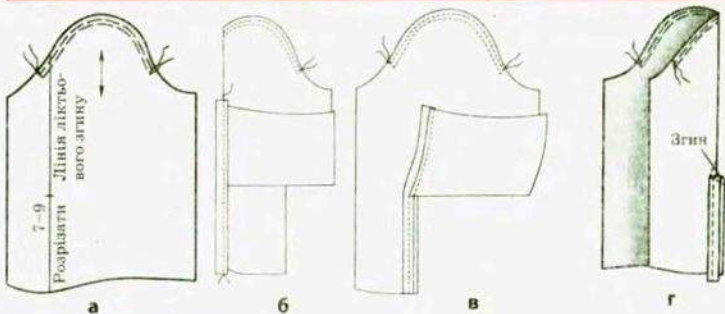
Обробка розрізу на рукаві обшивкою
